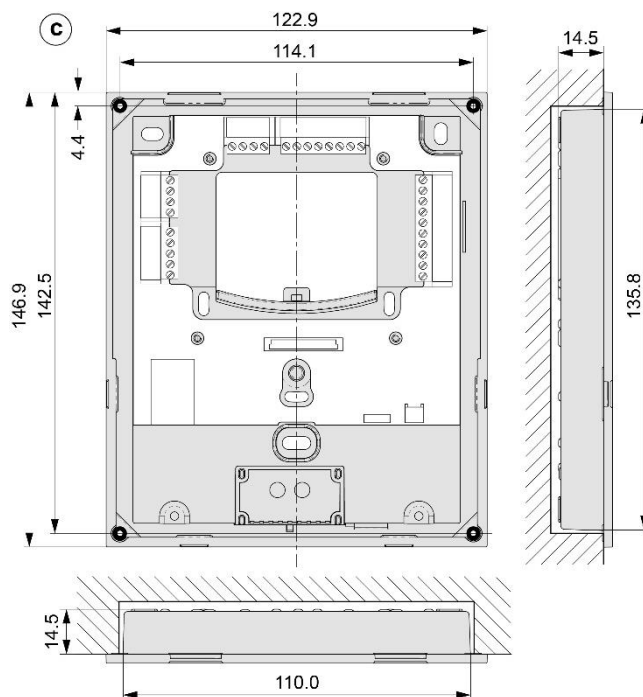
Halbversenkter Einbau (Maße in mm)
